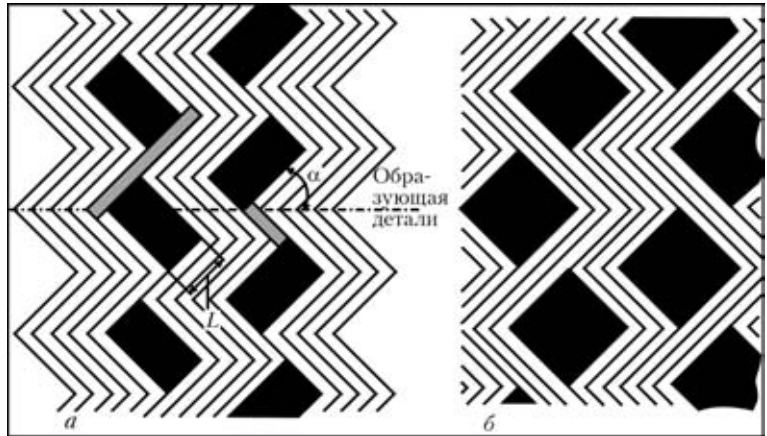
Схемы (а, б) формирования лунок при наплавке рабочей поверхности швами зигзагообразной формы
